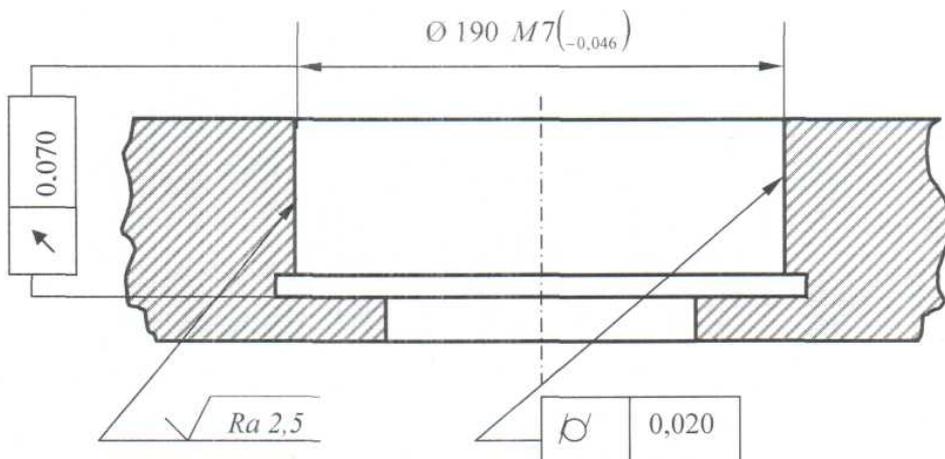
Обозначение допусков размера отверстия в корпусе
